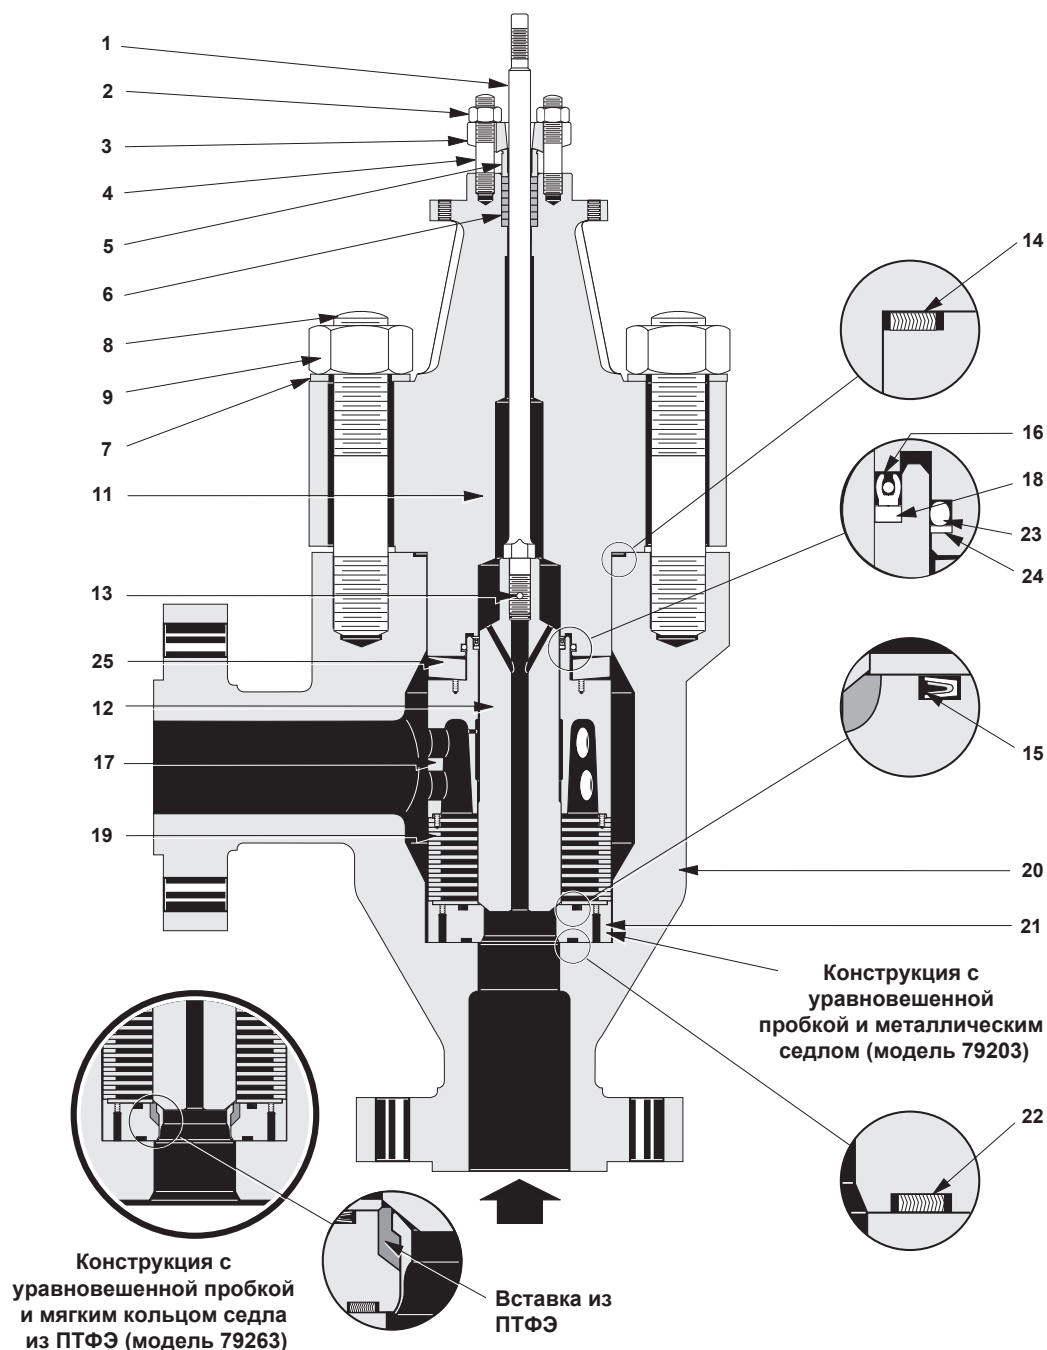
Поперечное сечение клапана VRT серии 79000 размером 6 дюймов с литым корпусом
